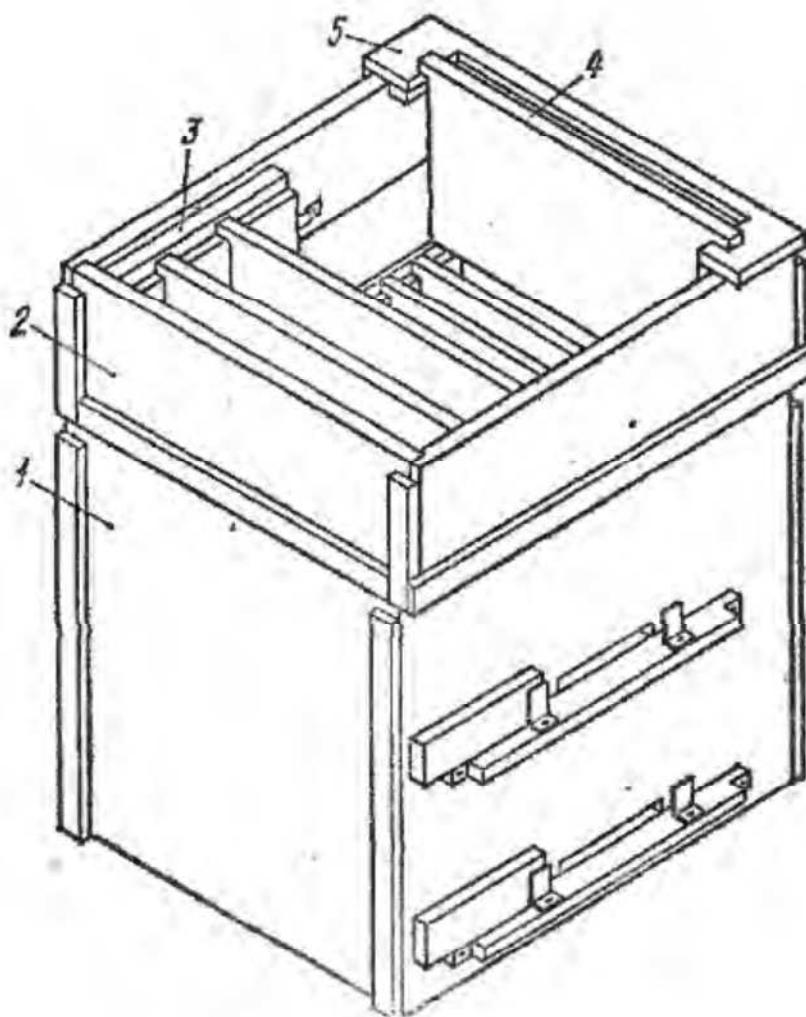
Улей двухкорпусный с вкладышами (общий вид со снятой крышкой)!
